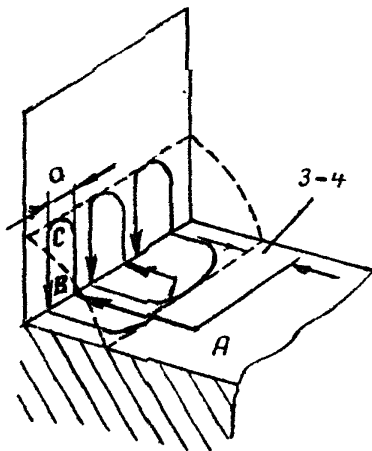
Схема движения электрода при сварке угловых швов тавровых и нахлесточных соединений
